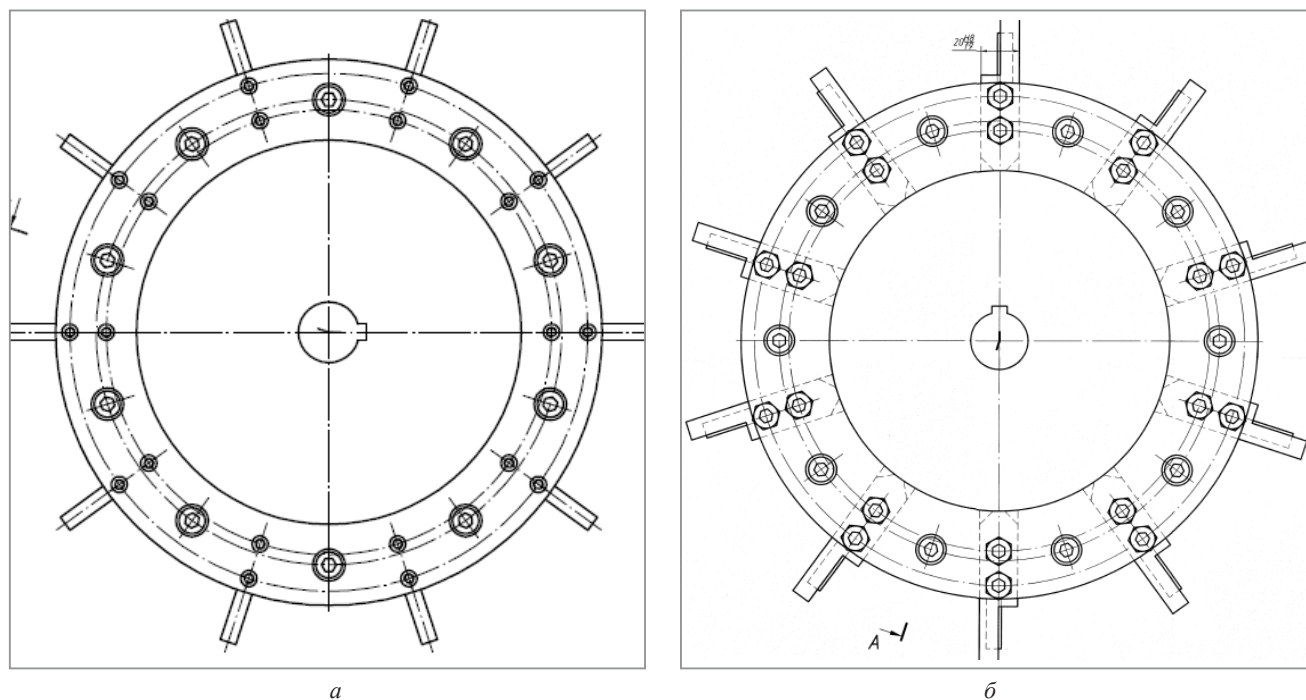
Конструкции крепления ножей: а – крепление ножей по конструкции завода-изготовителя; б – крепление ножей (с адаптером) по предложенной конструкции
